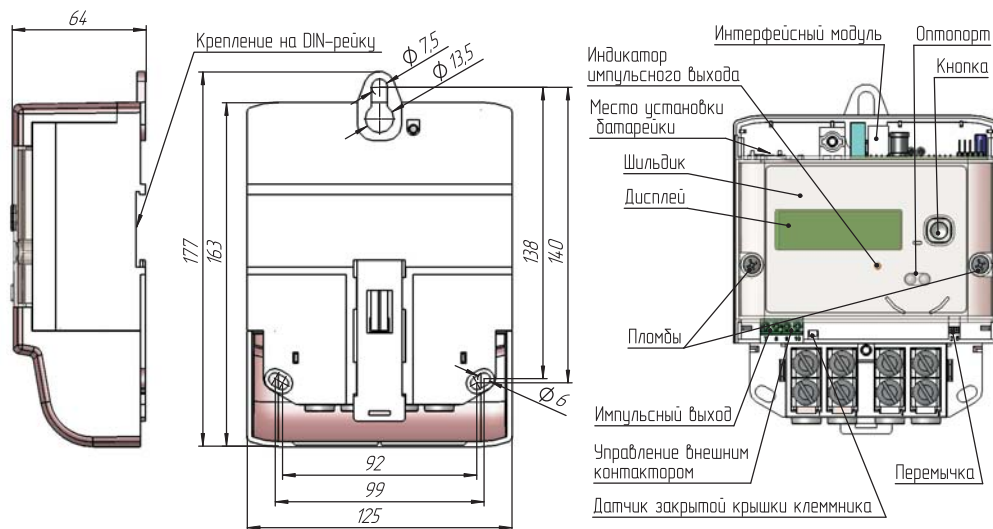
Общий вид, габаритные и установочные размеры, места установки пломб на корпусе однофазного счетчика типа МТХ1
